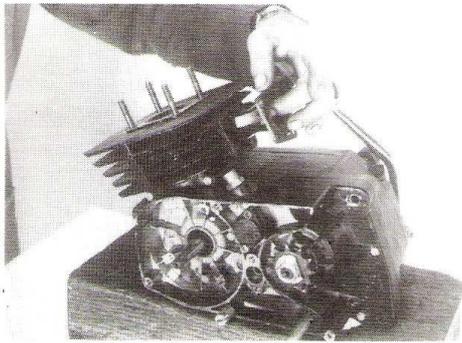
Manualmente desmontar la boquilla carburador y el conjunto soporte válvula admisión.
